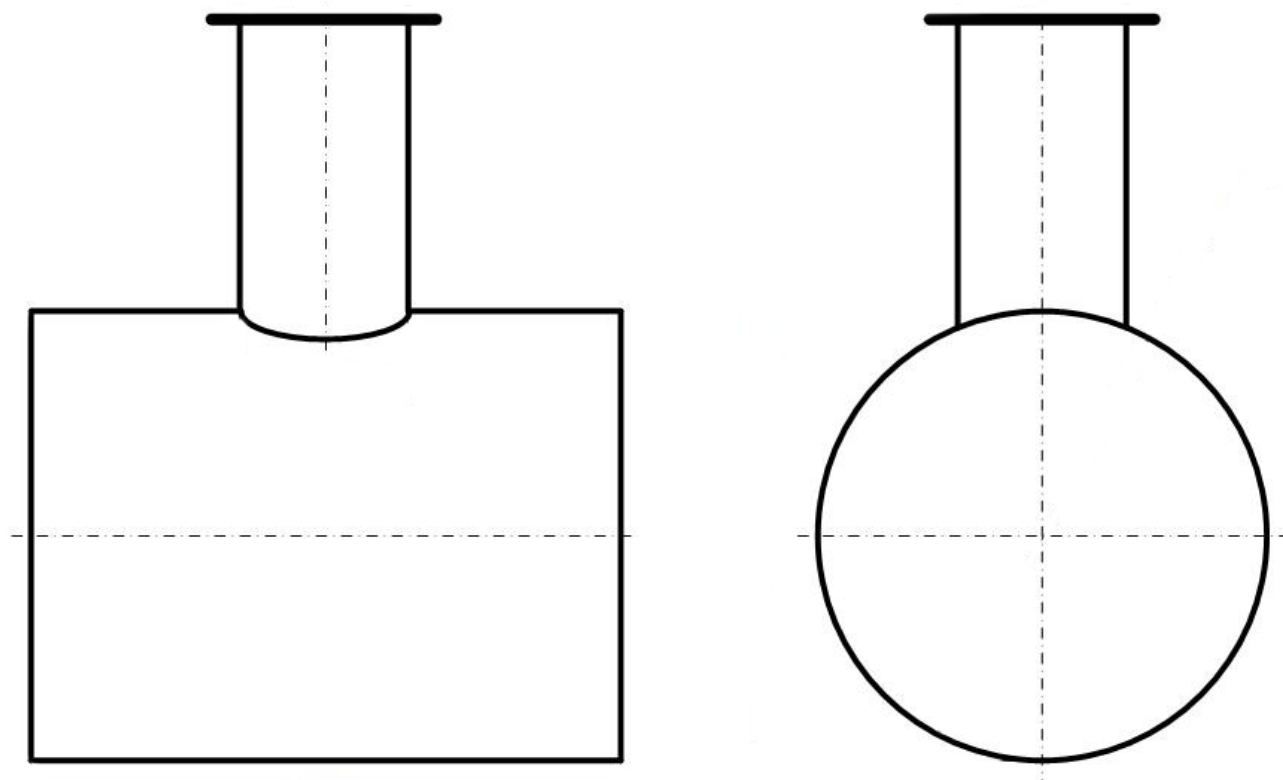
Общий вид эскиза резервуара РГС-3
